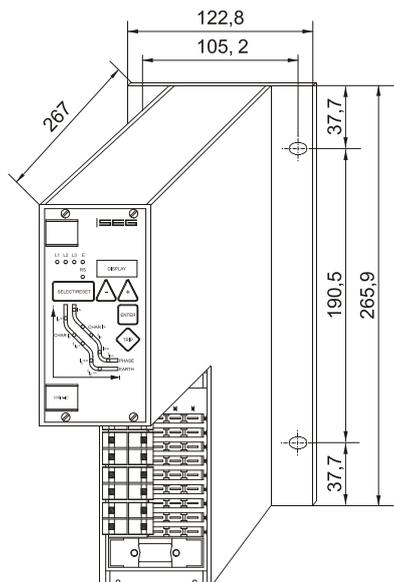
Baugruppenträger für Montageplattenaufbau mit Relaisvariante A, 12 TE
